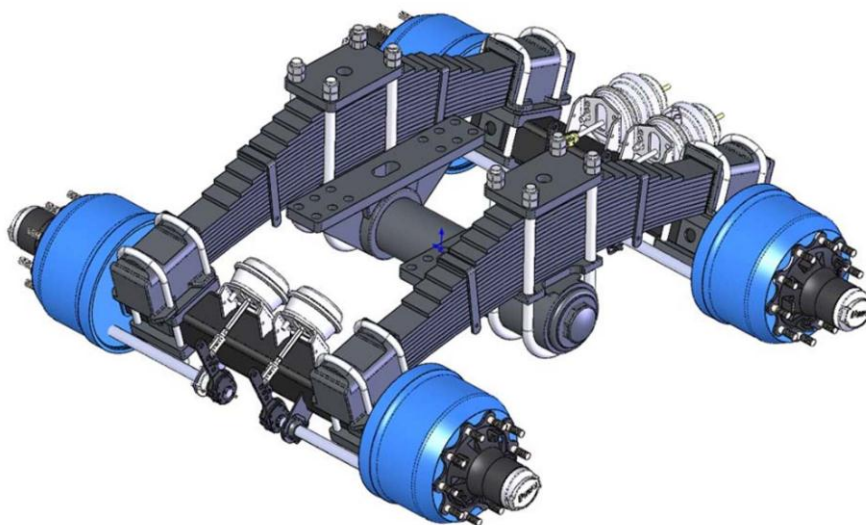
Рессорно-балансирная подвеска без реактивных штанг
